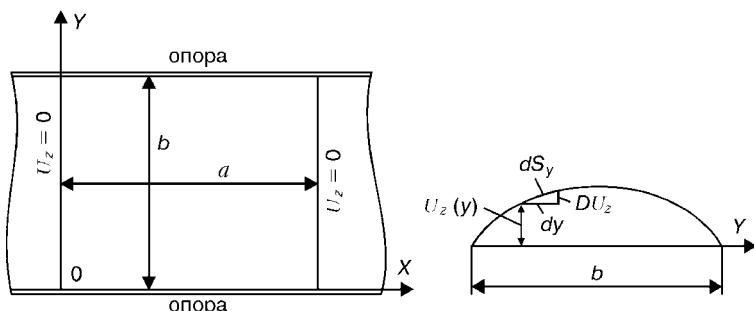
Схема участка сварной конструкции размером $a \times b$ с деформацией бухтиноватости
